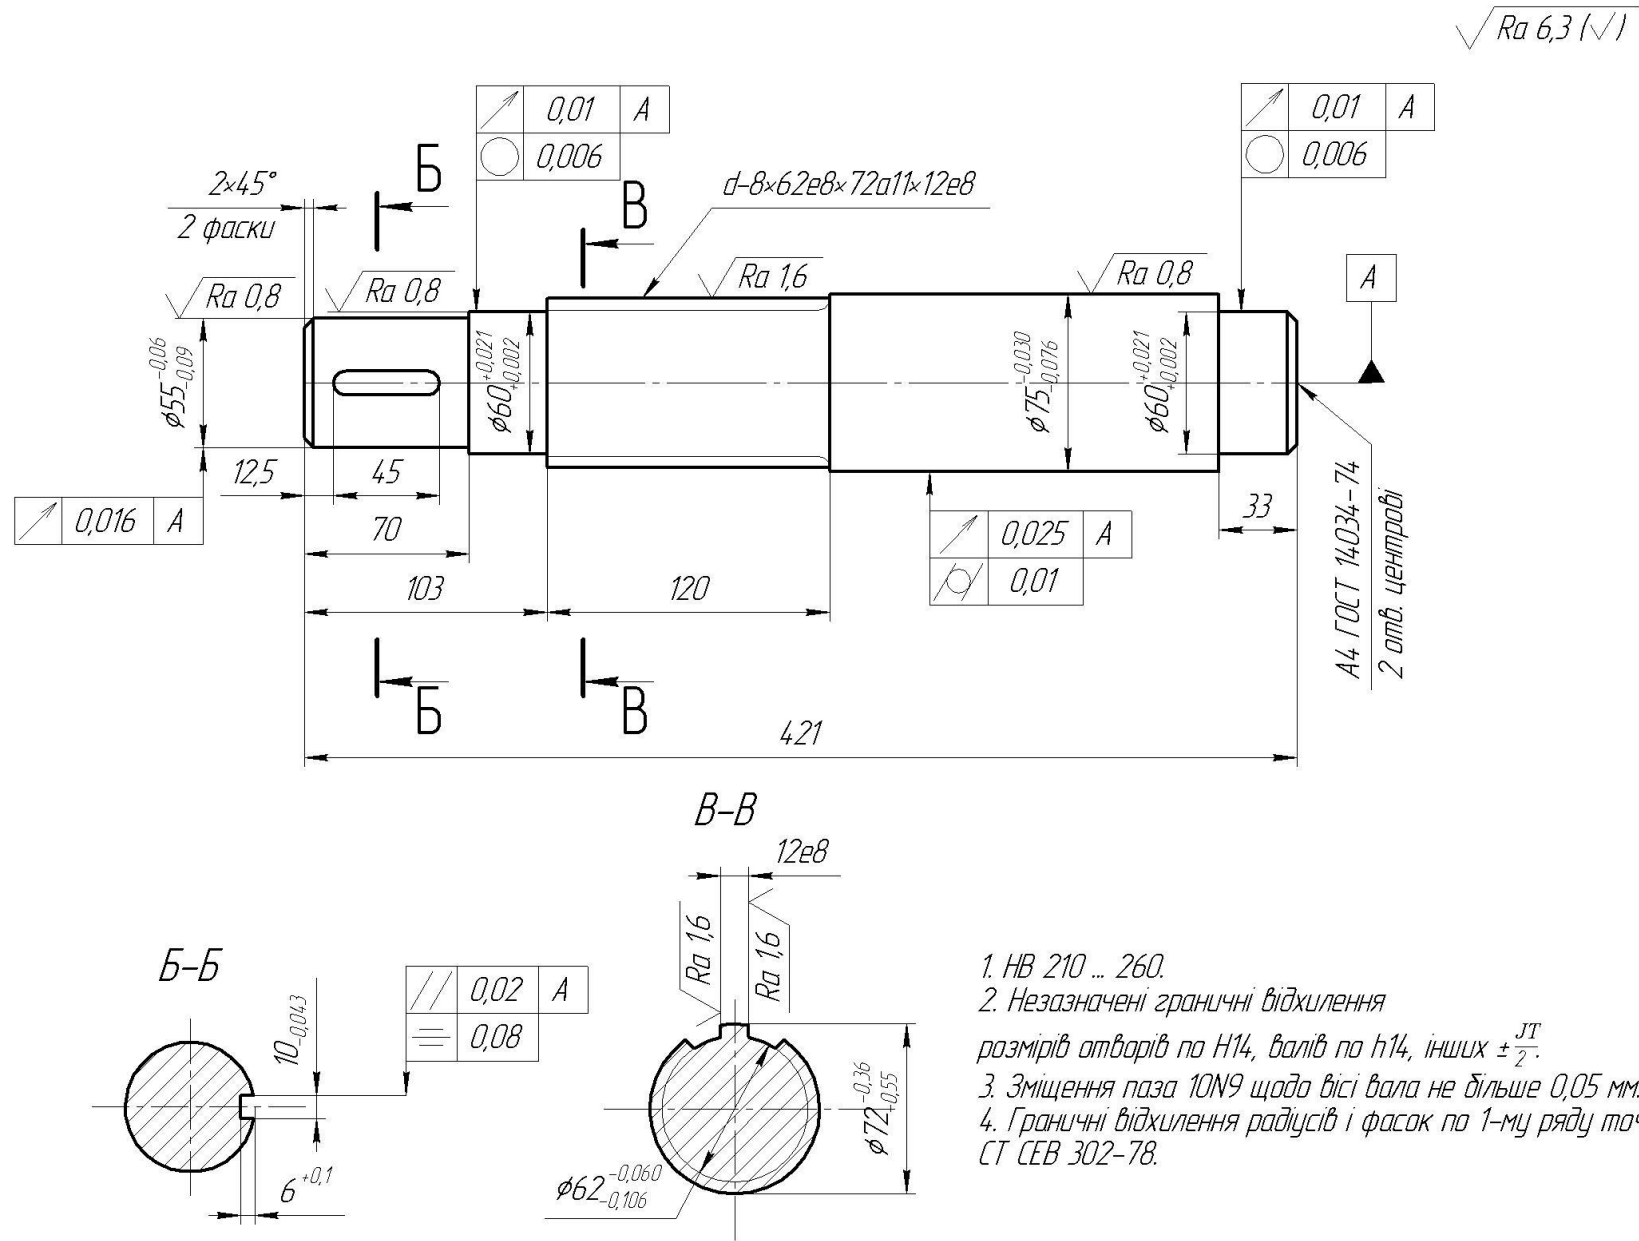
Кресленник деталі «Вал шліцьовий»
